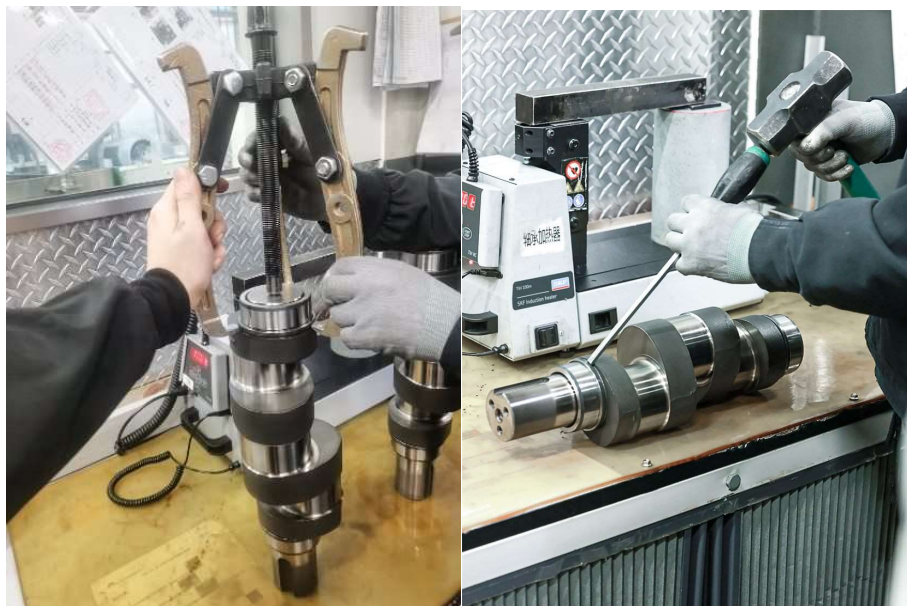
Съём и установка внутренних колец подшипников коленчатого вала
